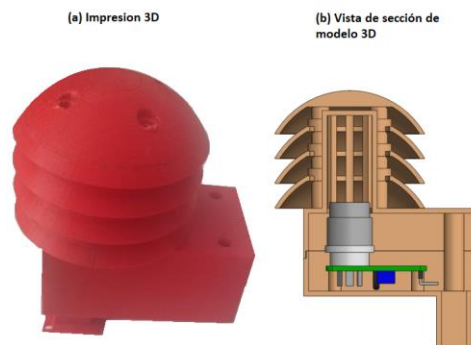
Carcasa para sensor MG811, (a) Impresión 3D, (b) Vista de sección [39].
